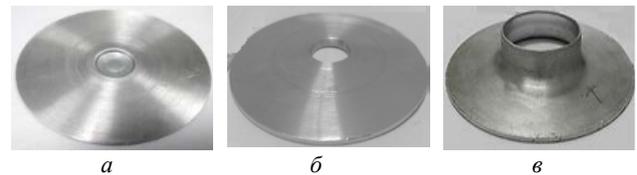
Профільована заготовка з перемичкою (*a*), профільована заготовка з отвором (*b*) деталь з фланцем після відбортування (*в*)
